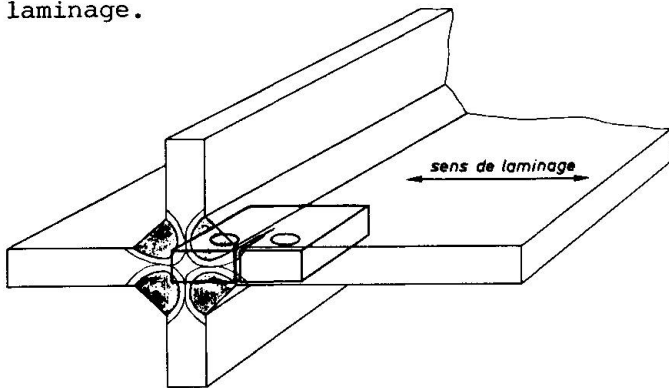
Prélèvement des éprouvettes dans les joints soudés en croix
